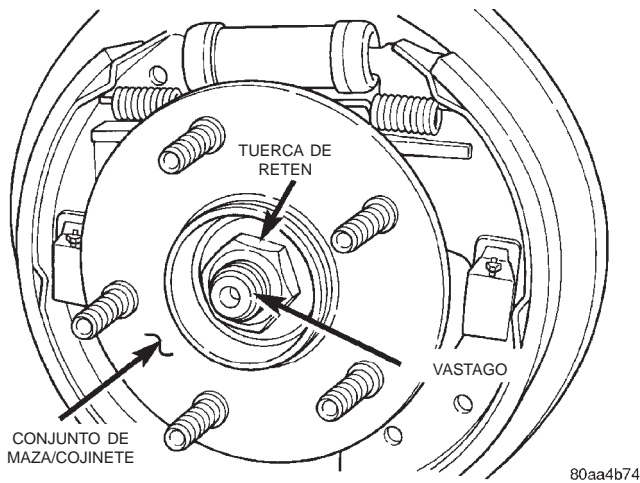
Tuerca de retén del conjunto de maza/cojinete
